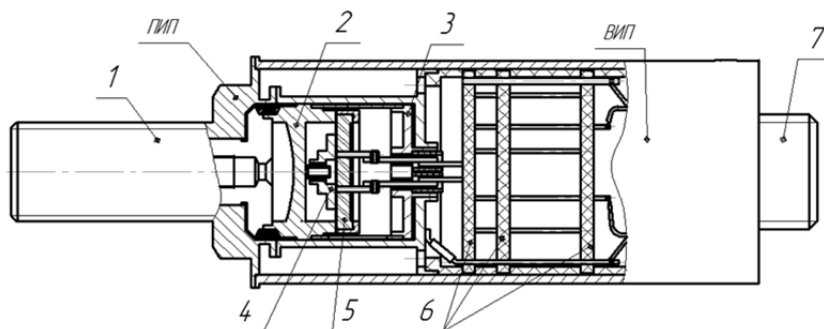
Емкостный датчик давления: 1 – штуцер; 2 – мембрана; 3 – гермопереходник; 4 – подвижная обкладка конденсатора; 5 – неподвижная обкладка конденсатора; 6 – платы; 7 – вилка; ПИП – первичный измерительный преобразователь; ВИП – вторичный измерительный преобразователь
